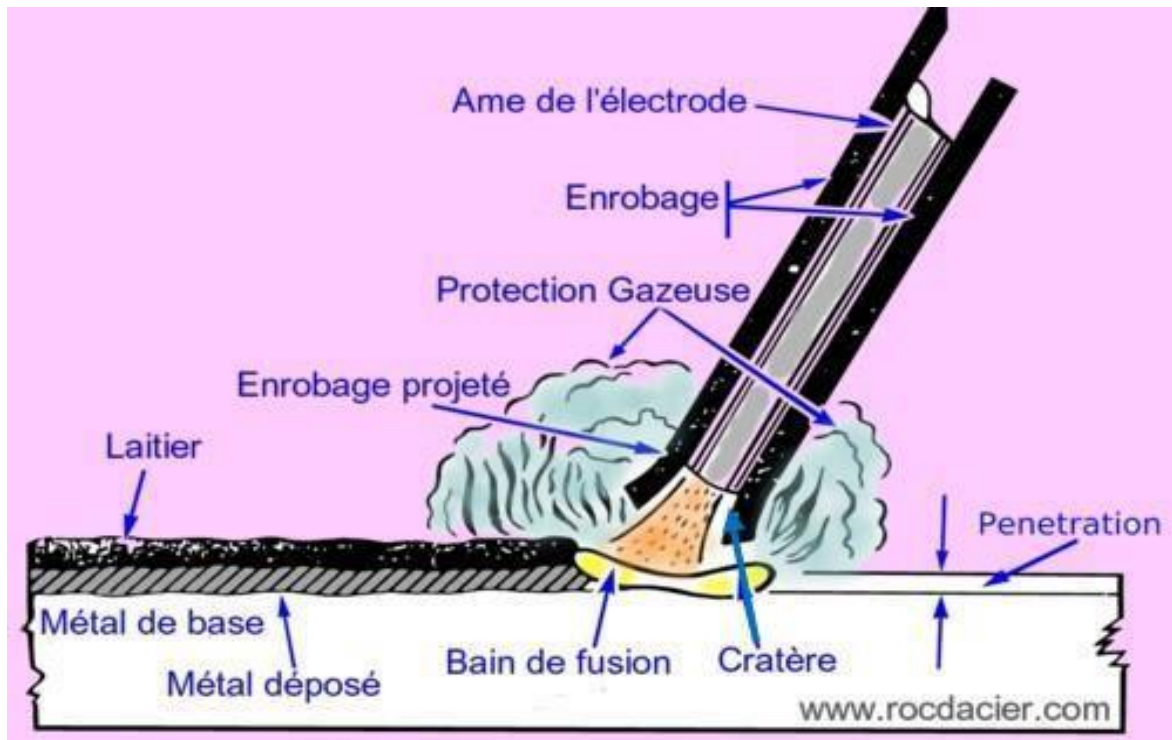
Principe de l'opération de soudage SMAW
